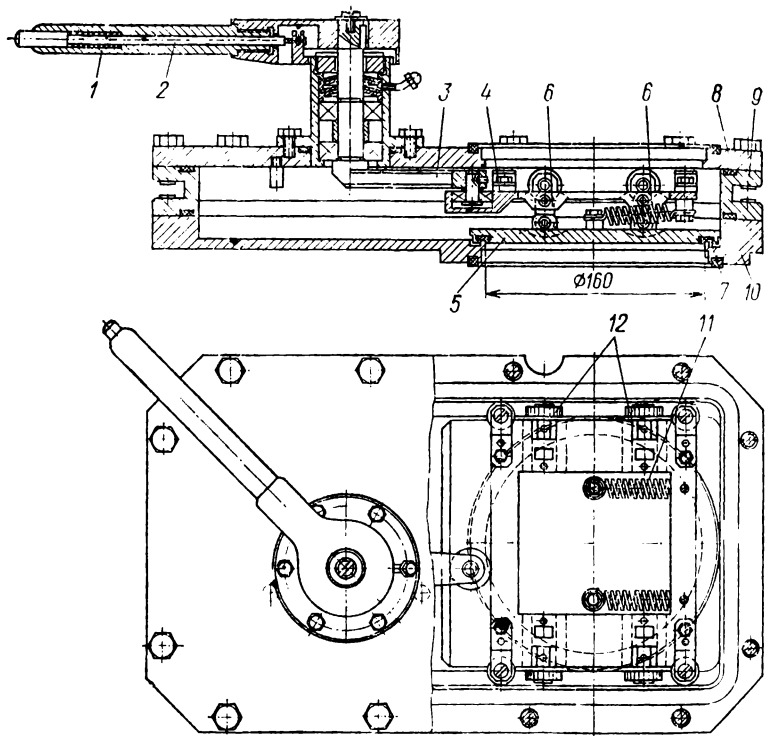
Вакуумный затвор с малыми осевыми размерами.
